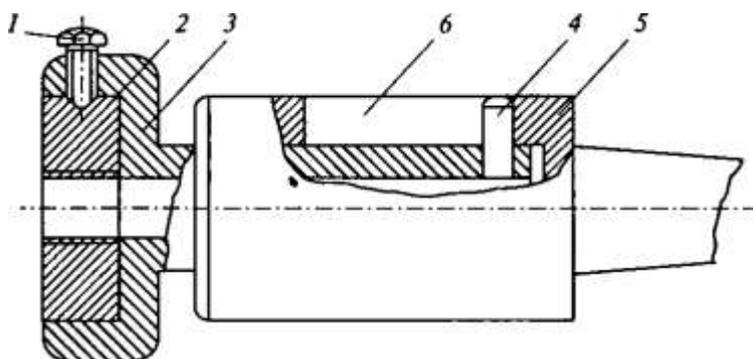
Плашкодержатель для резбонарезного инструмента:
